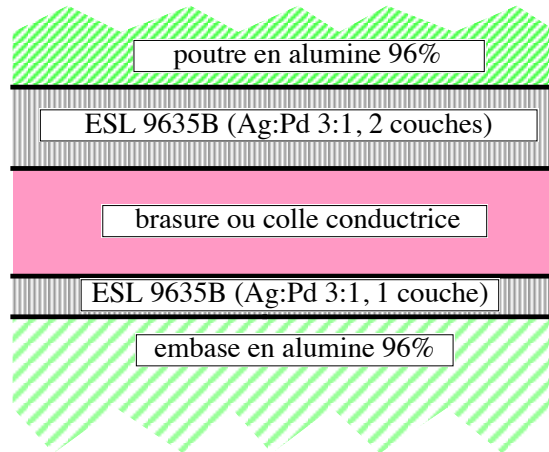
Empilement des couches intervenant dans l'assemblage de la poutre sur l'embase.
